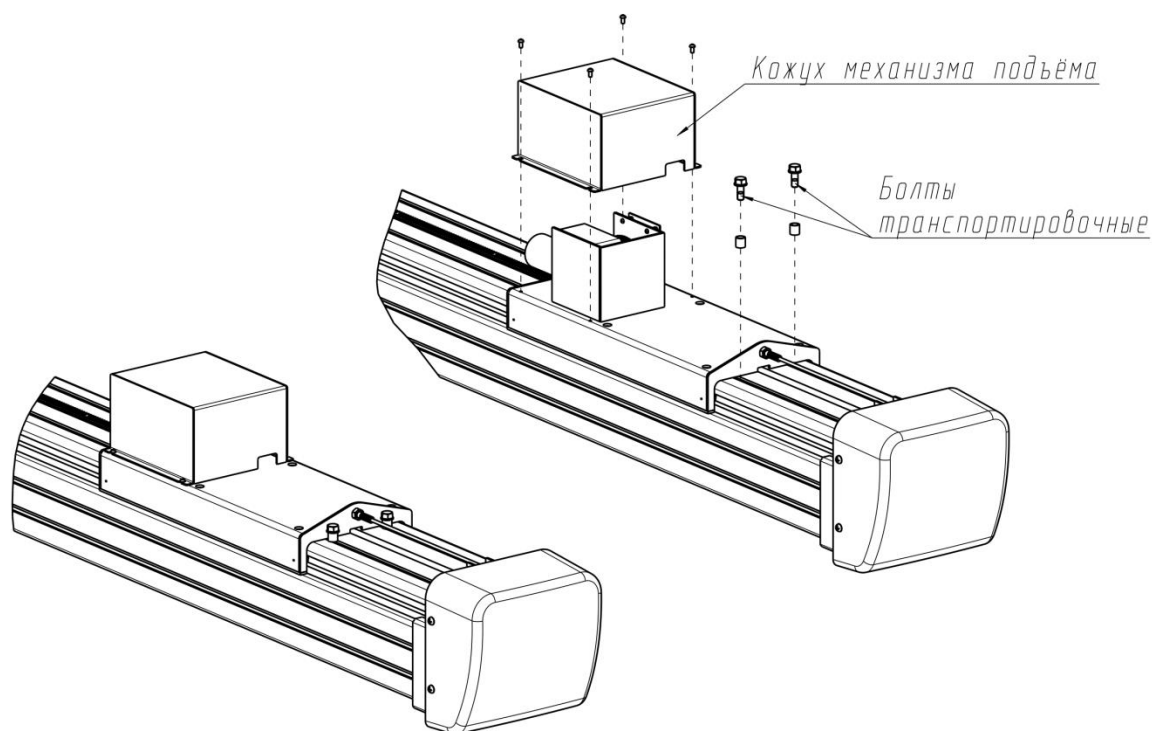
Демонтаж болтов и кожуха механизма подъема
